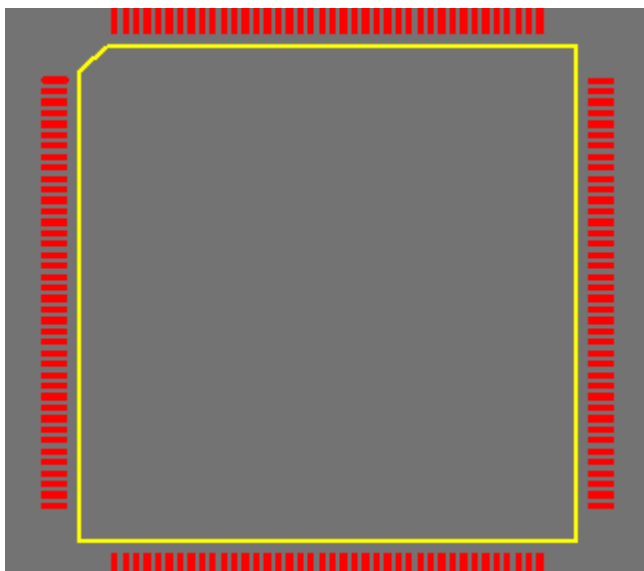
生成的 S3C44B0 芯片的 PCB 封装
